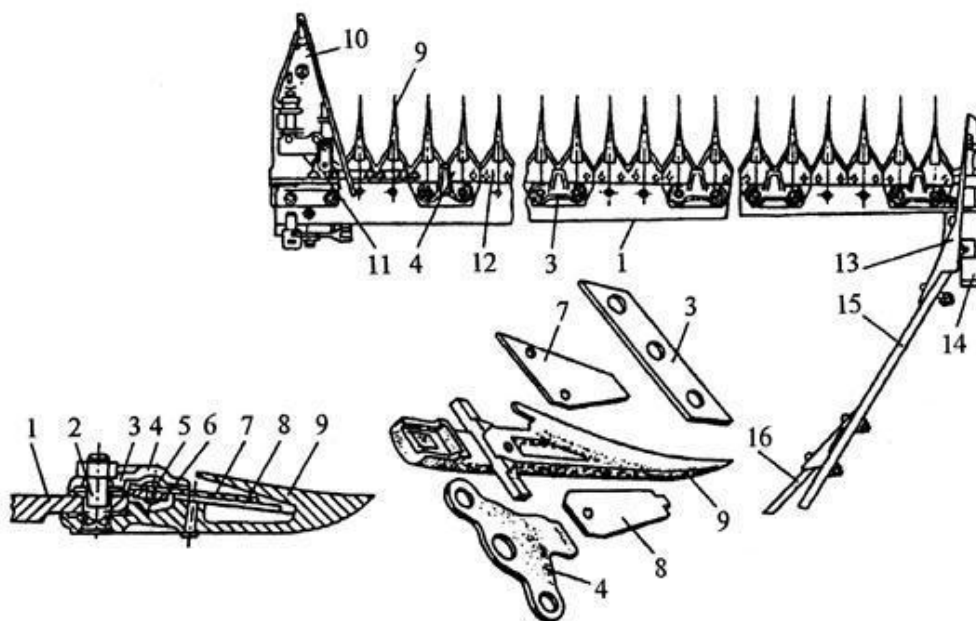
Режущий аппарат сегментно-пальцевого типа косилки: 1 – пальцевый брус; 2 – болт; 3 – пластина трения; 4 – прижимная лапка; 5 – заклепка; 6 – спинка ножа; 7 – сегмент; 8 – противорежущая пластина; 9 – палец; 10 – внутренний делитель; 11 – головка ножа; 12 – нож; 13 – внешний делитель; 14 – опорный салазки; 15 – полевая доска; 16 – прутки-стеблеотводы
